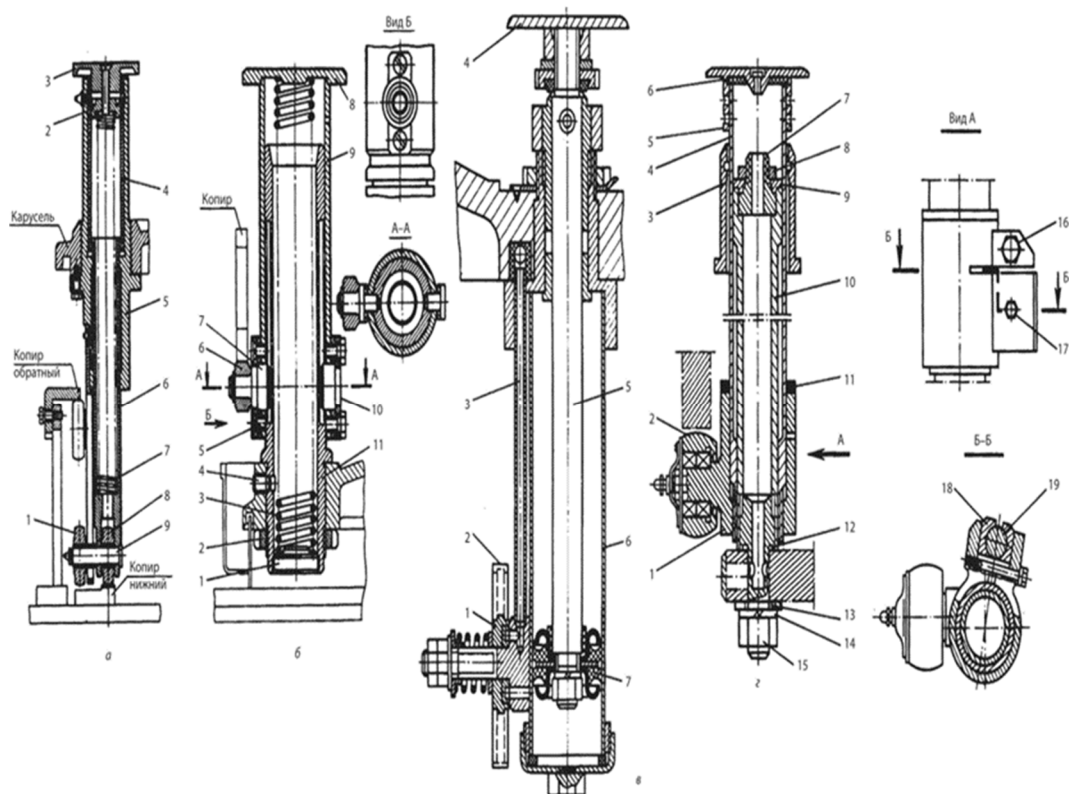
Підйомні столики фасувальних машин: а - Т1-ВРА-6А: 1,8 - ролики; 2 - гайка; 3 - столик; 4 - гільза; 5 - корпус; 6 - шток; 7- пружина; 9 - вісь; б - ВАР-6: 1, 2 - гайки; 3 - пружина; 4,5 - гвинти; 6 - ролик; 7,10 - шпонки; 8 - столик; 9 - склянка; 11 - гільза; в - ВД2Р-6: 1 - золотник; 2 - зірочка; 3 - трубка; 4 - столик; 5 - шток; 6 - циліндр; 7 - поршень; з - Т1-ВДР-12В: 1 - кронштейн; 2 - ролик; 3 - втулка; 4, 10 - трубки; 5 - контр-гайка; 6 - майданчик; 7-кришка; 8, 15-гайки; 9 - манжета; 11-амортизатор; 12 - кільця; 13, 14 - шайби, 16, 17 - болти; 18 - сухар; 19 - шток
